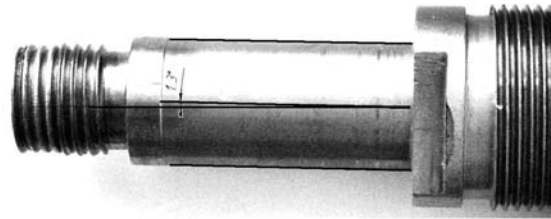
Переходная шпилька для крепления приспособления для реализации импульсных погрузок образца к траверсам установки
